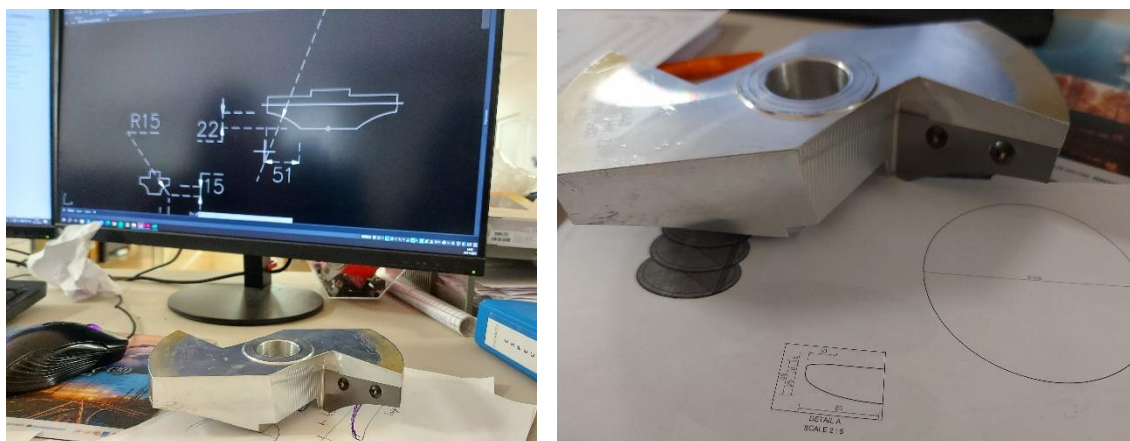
Da esquerda para a direita: Desenho técnico feito em Autocad do molde de corte utilizado na CNC, na direita o molde físico do molde de corte da mesa de centro "DUPLEX" e "TRIPLEX" utilizado na CNC.
